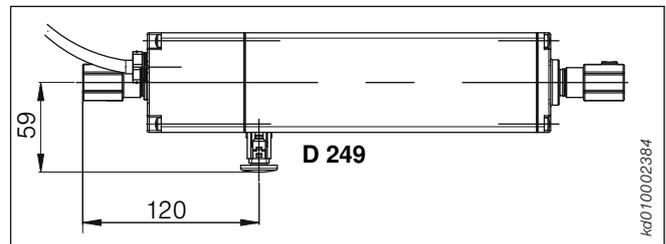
Maßanleitung Raffstore-Mittelmotor Typ D 249
